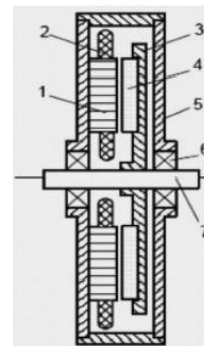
Descriptif de la machine à flux axial 1 stator / 1 rotor [13].
